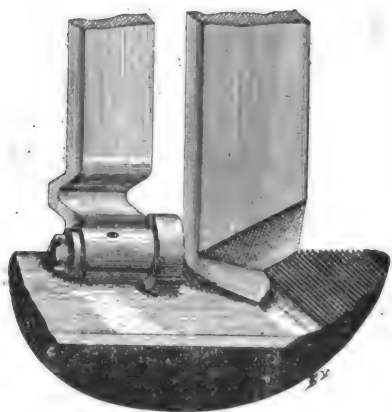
Burin et galet mobile de la machine à raboter Majert.
